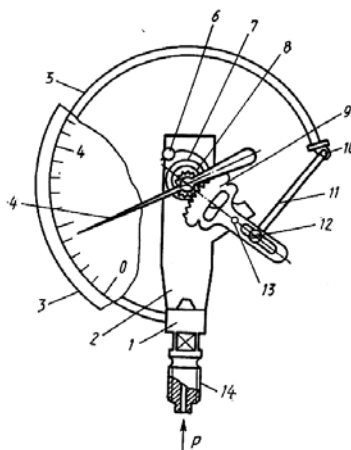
Схема манометра с одновитковой трубчатой пружиной
